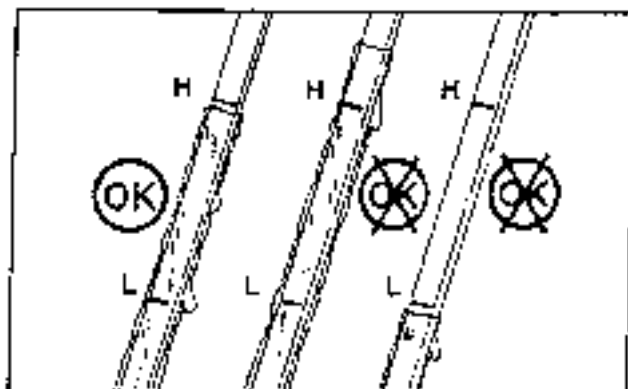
Прутковый мерный щуп для проверки уровня масла в поддоне двигателя
